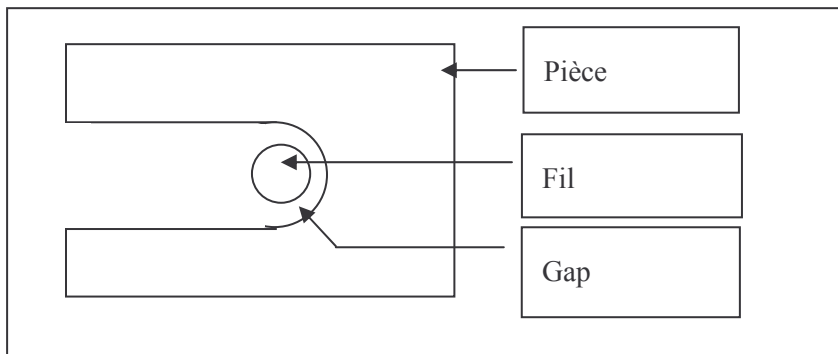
Vue de dessus de la pièce usinée en ébauche
